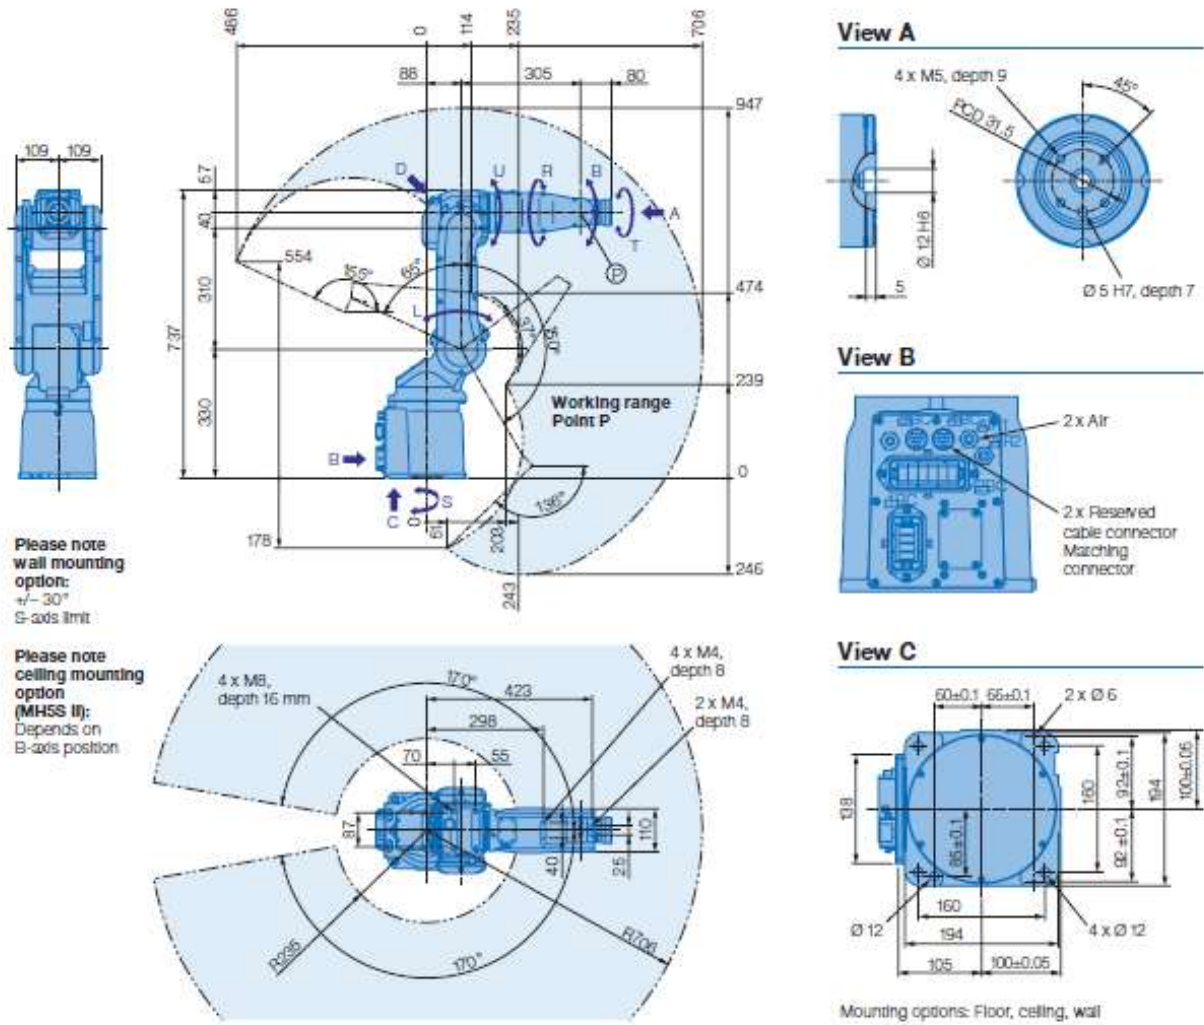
Dimensiones Fuente: Yaskawa Motoman
